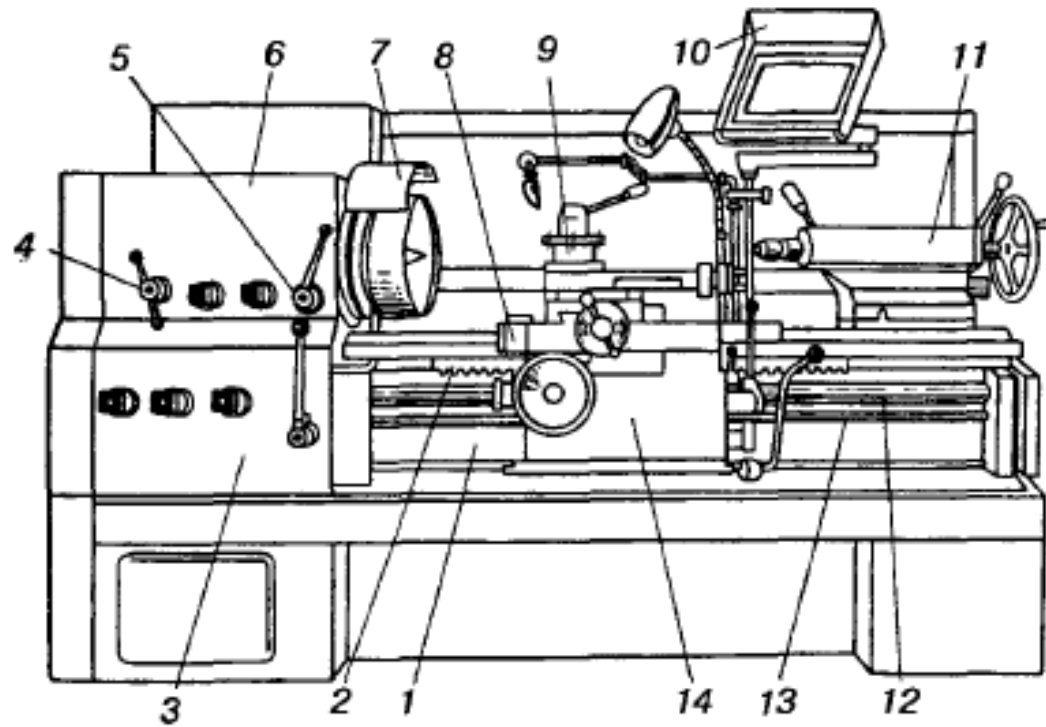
Загальний вигляд токарно-гвинторізного верстата 16К20
